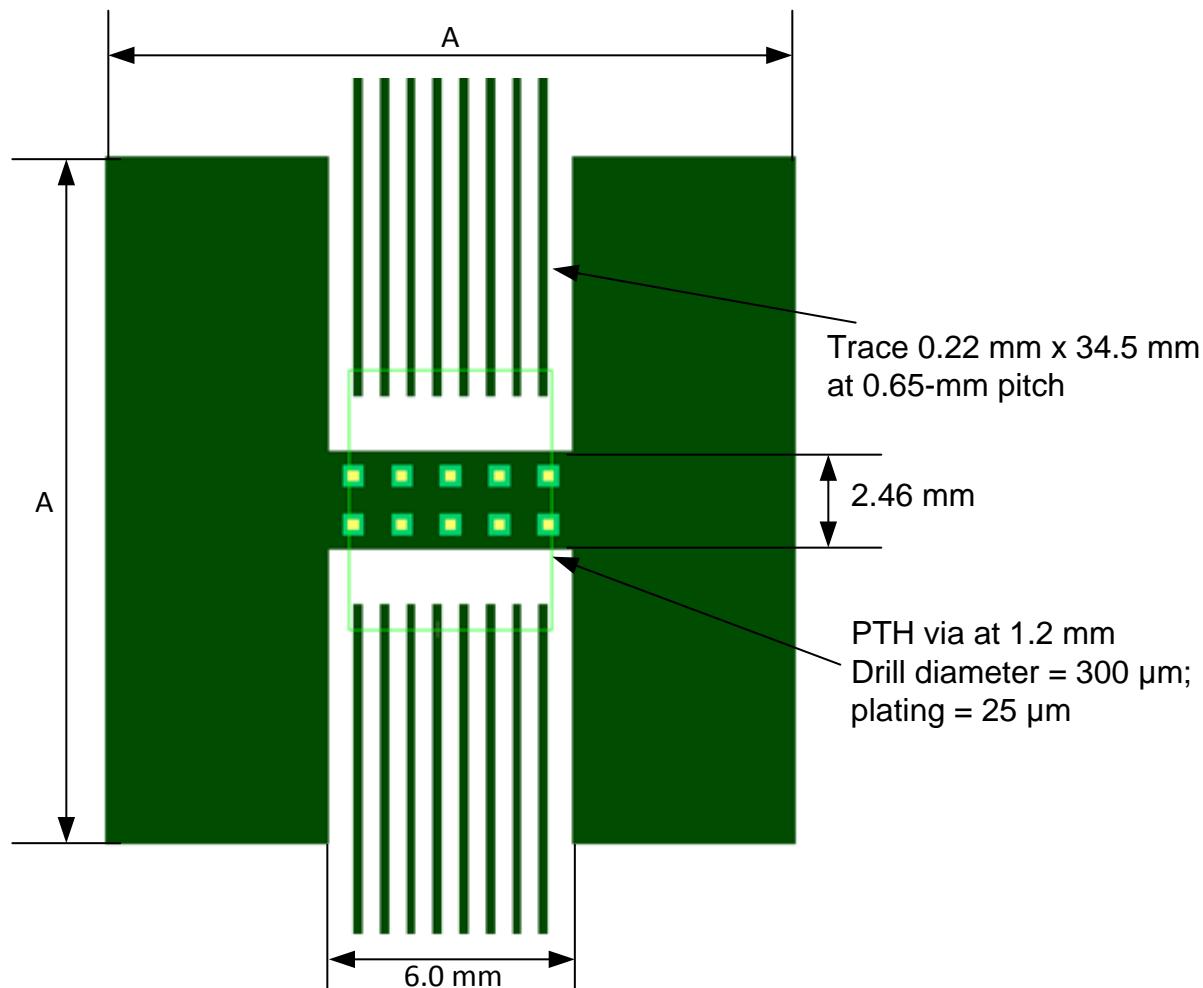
PCB モデル (4 層 PCB を表示、2 層 PCB はビアなし)
